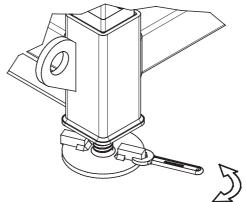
Regolazione dell'altezza dei piedi con una chiave a tubo da 22 mm.
